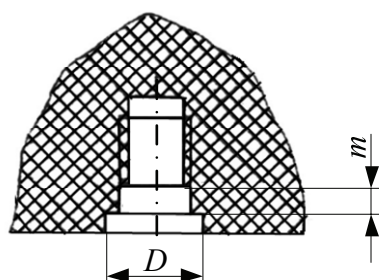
Участки цилиндрической поверхности на резьбовых отверстиях
